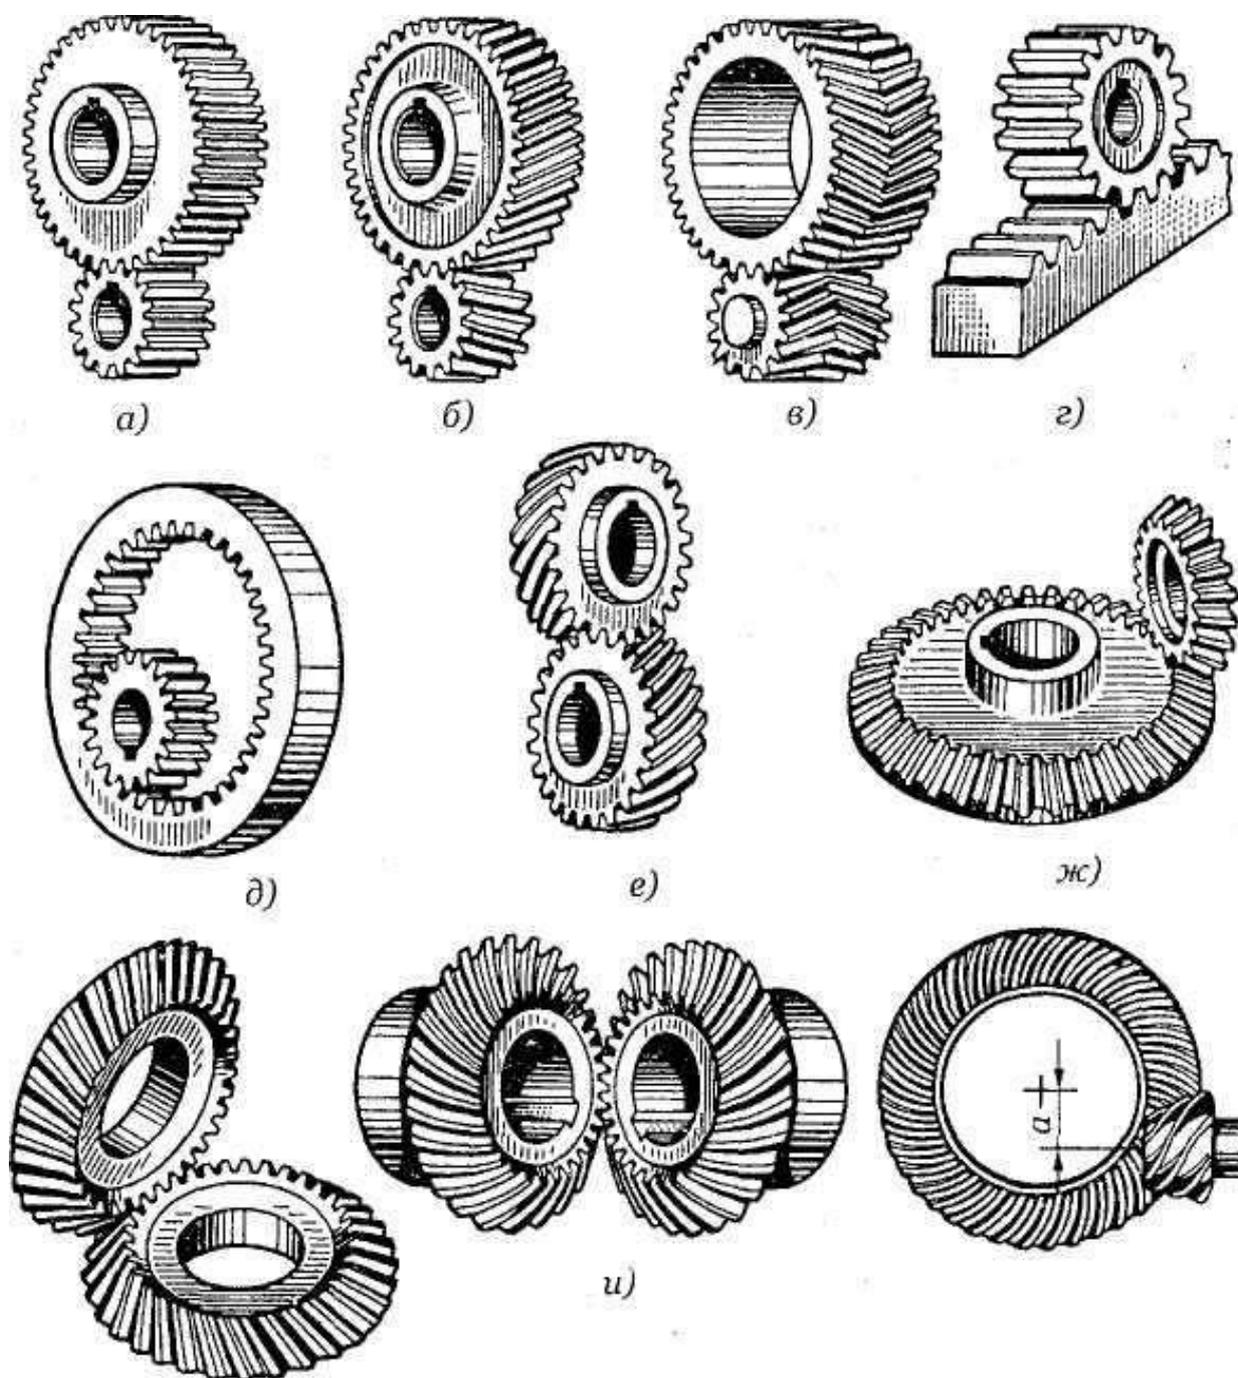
Виды зубчатых передач: *a, б, в* - цилиндрические зубчатые передачи с внешним зацеплением; *г* - реечная передача; *д* - цилиндрическая передача с внутренним зацеплением; *е* - зубчатая винтовая передача; *ж, з, и* - конические зубчатые передачи
